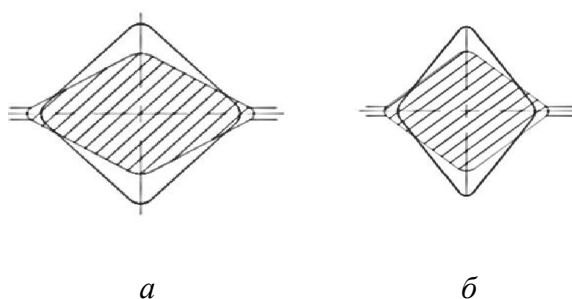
Схема прокатки для системы чередующихся калибров «ромб–квадрат»:
